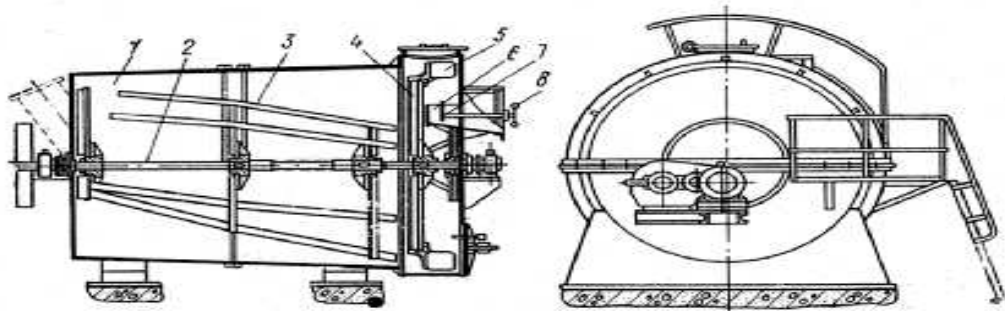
Ковшовая мешалка: 1 – корпус; 2 – вал; 3 – лопасти; 4 – колесо; 5 – ковши; 6 – коробка; 7 – заслонка; 8 – штурвал
